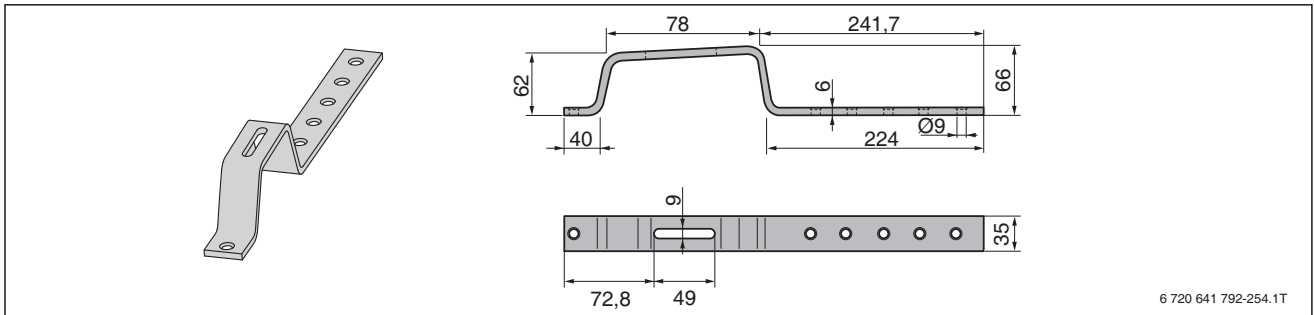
Sonderdachhaken für die Dachanbindung Schiefer-, Schindel-Eindeckung (Maße in mm)
